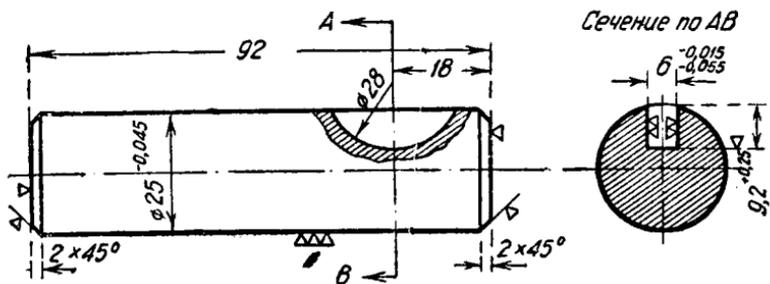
Дет. 18-33. Короткий валик вилки муфты сцепления
